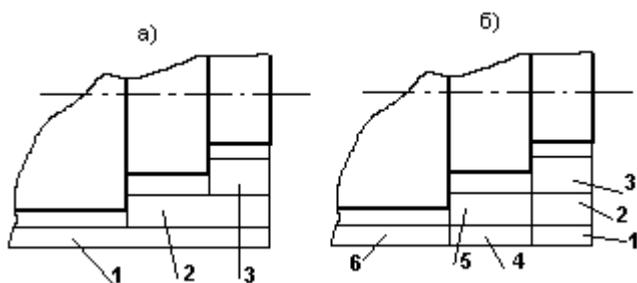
Варианты токарной обработки ступенчатых поверхностей
